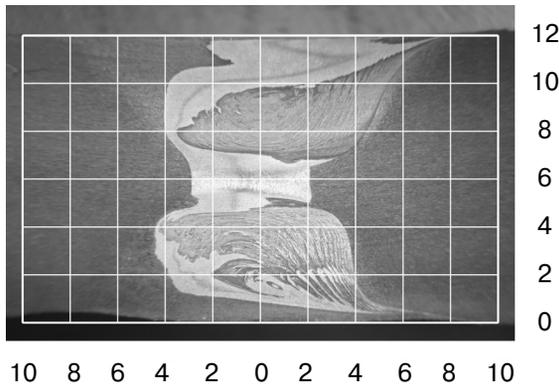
Макроструктура поперечного сечения стыкового сварного шва комбинации пластин 6082 - AMg5 - 6082
